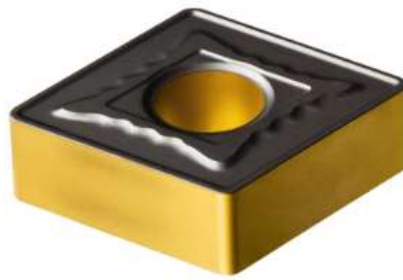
Пластина CNMG 12 04 08-MR 4405
